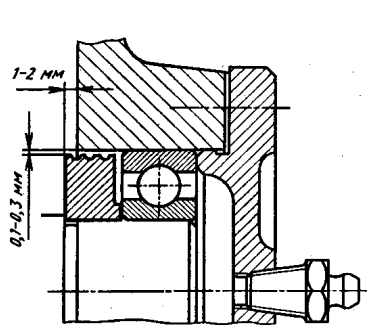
Узел подшипника с использованием пластичного смазочного материала
